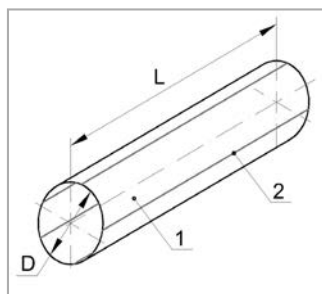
Схема сварной обечайки котла железнодорожной вагонцистерны, сваренной из листового полотна: 1 – лист; 2 – продольный сварной шов; D – внутренний диаметр обечайки; L – длина обечайки (длина продольного сварного шва)
